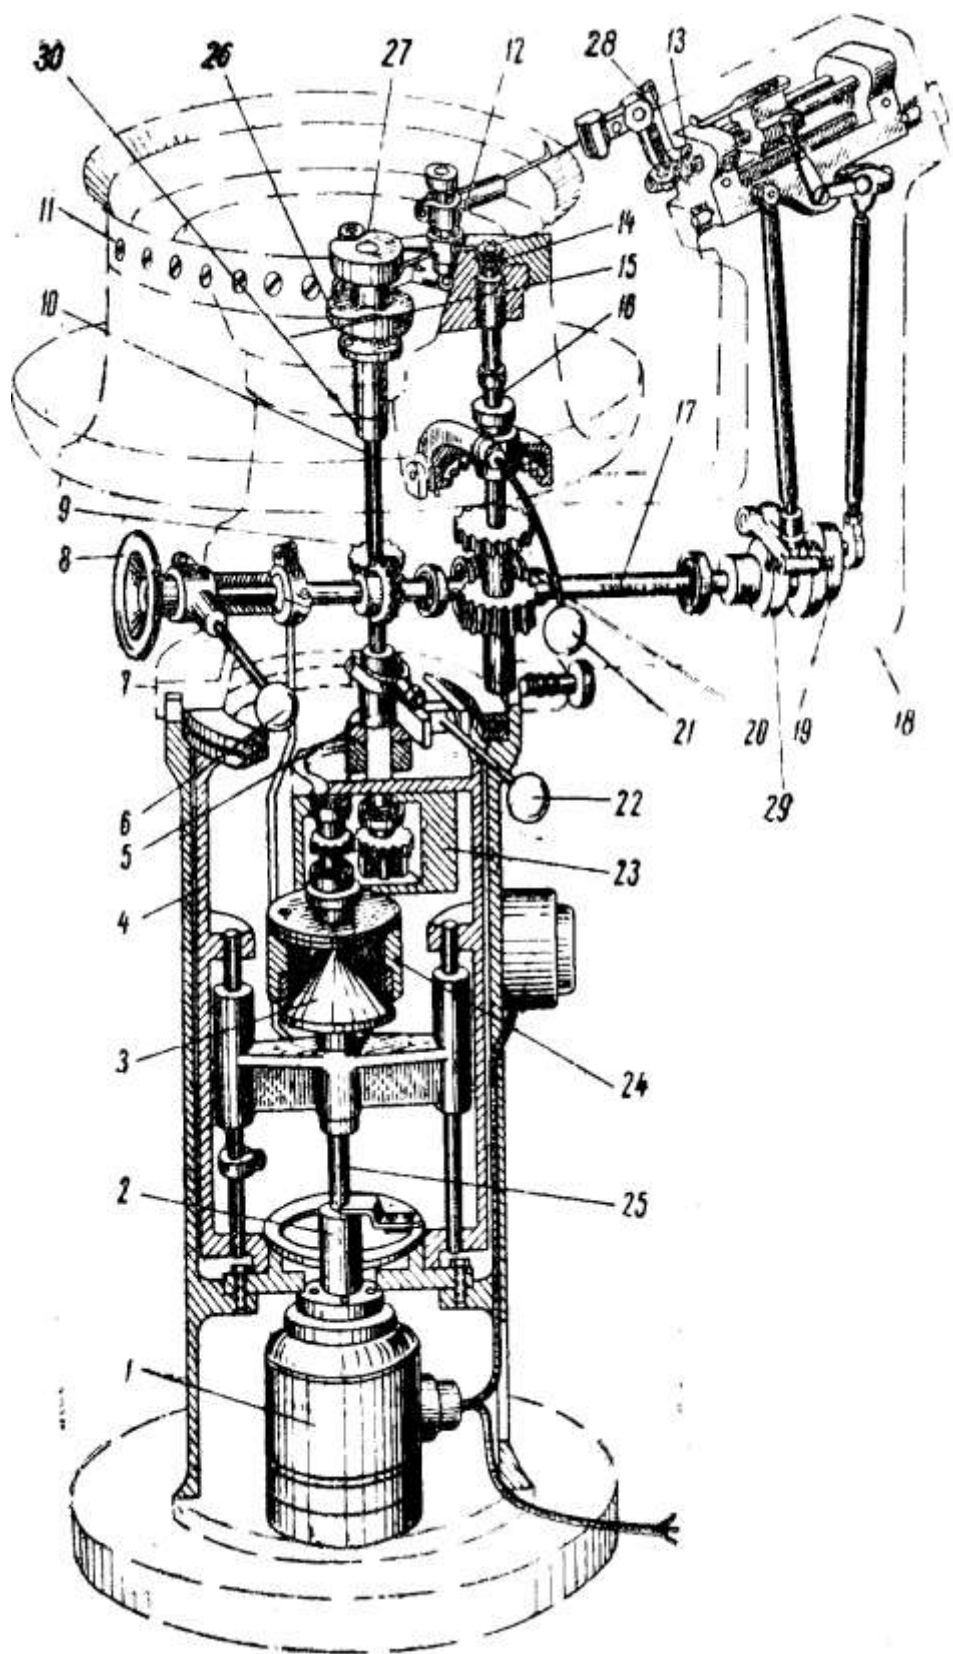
Конструктивно-кінематична схема КВТ-14
